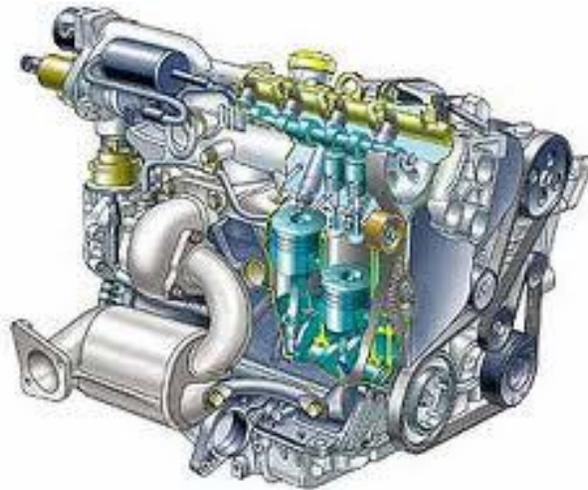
MOTOR RENAULT QUE FUE ACOPLADO CON COMPRESOR 2D
